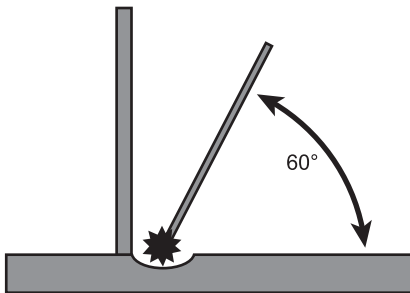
Сварка тонкого металла с более толстым.
